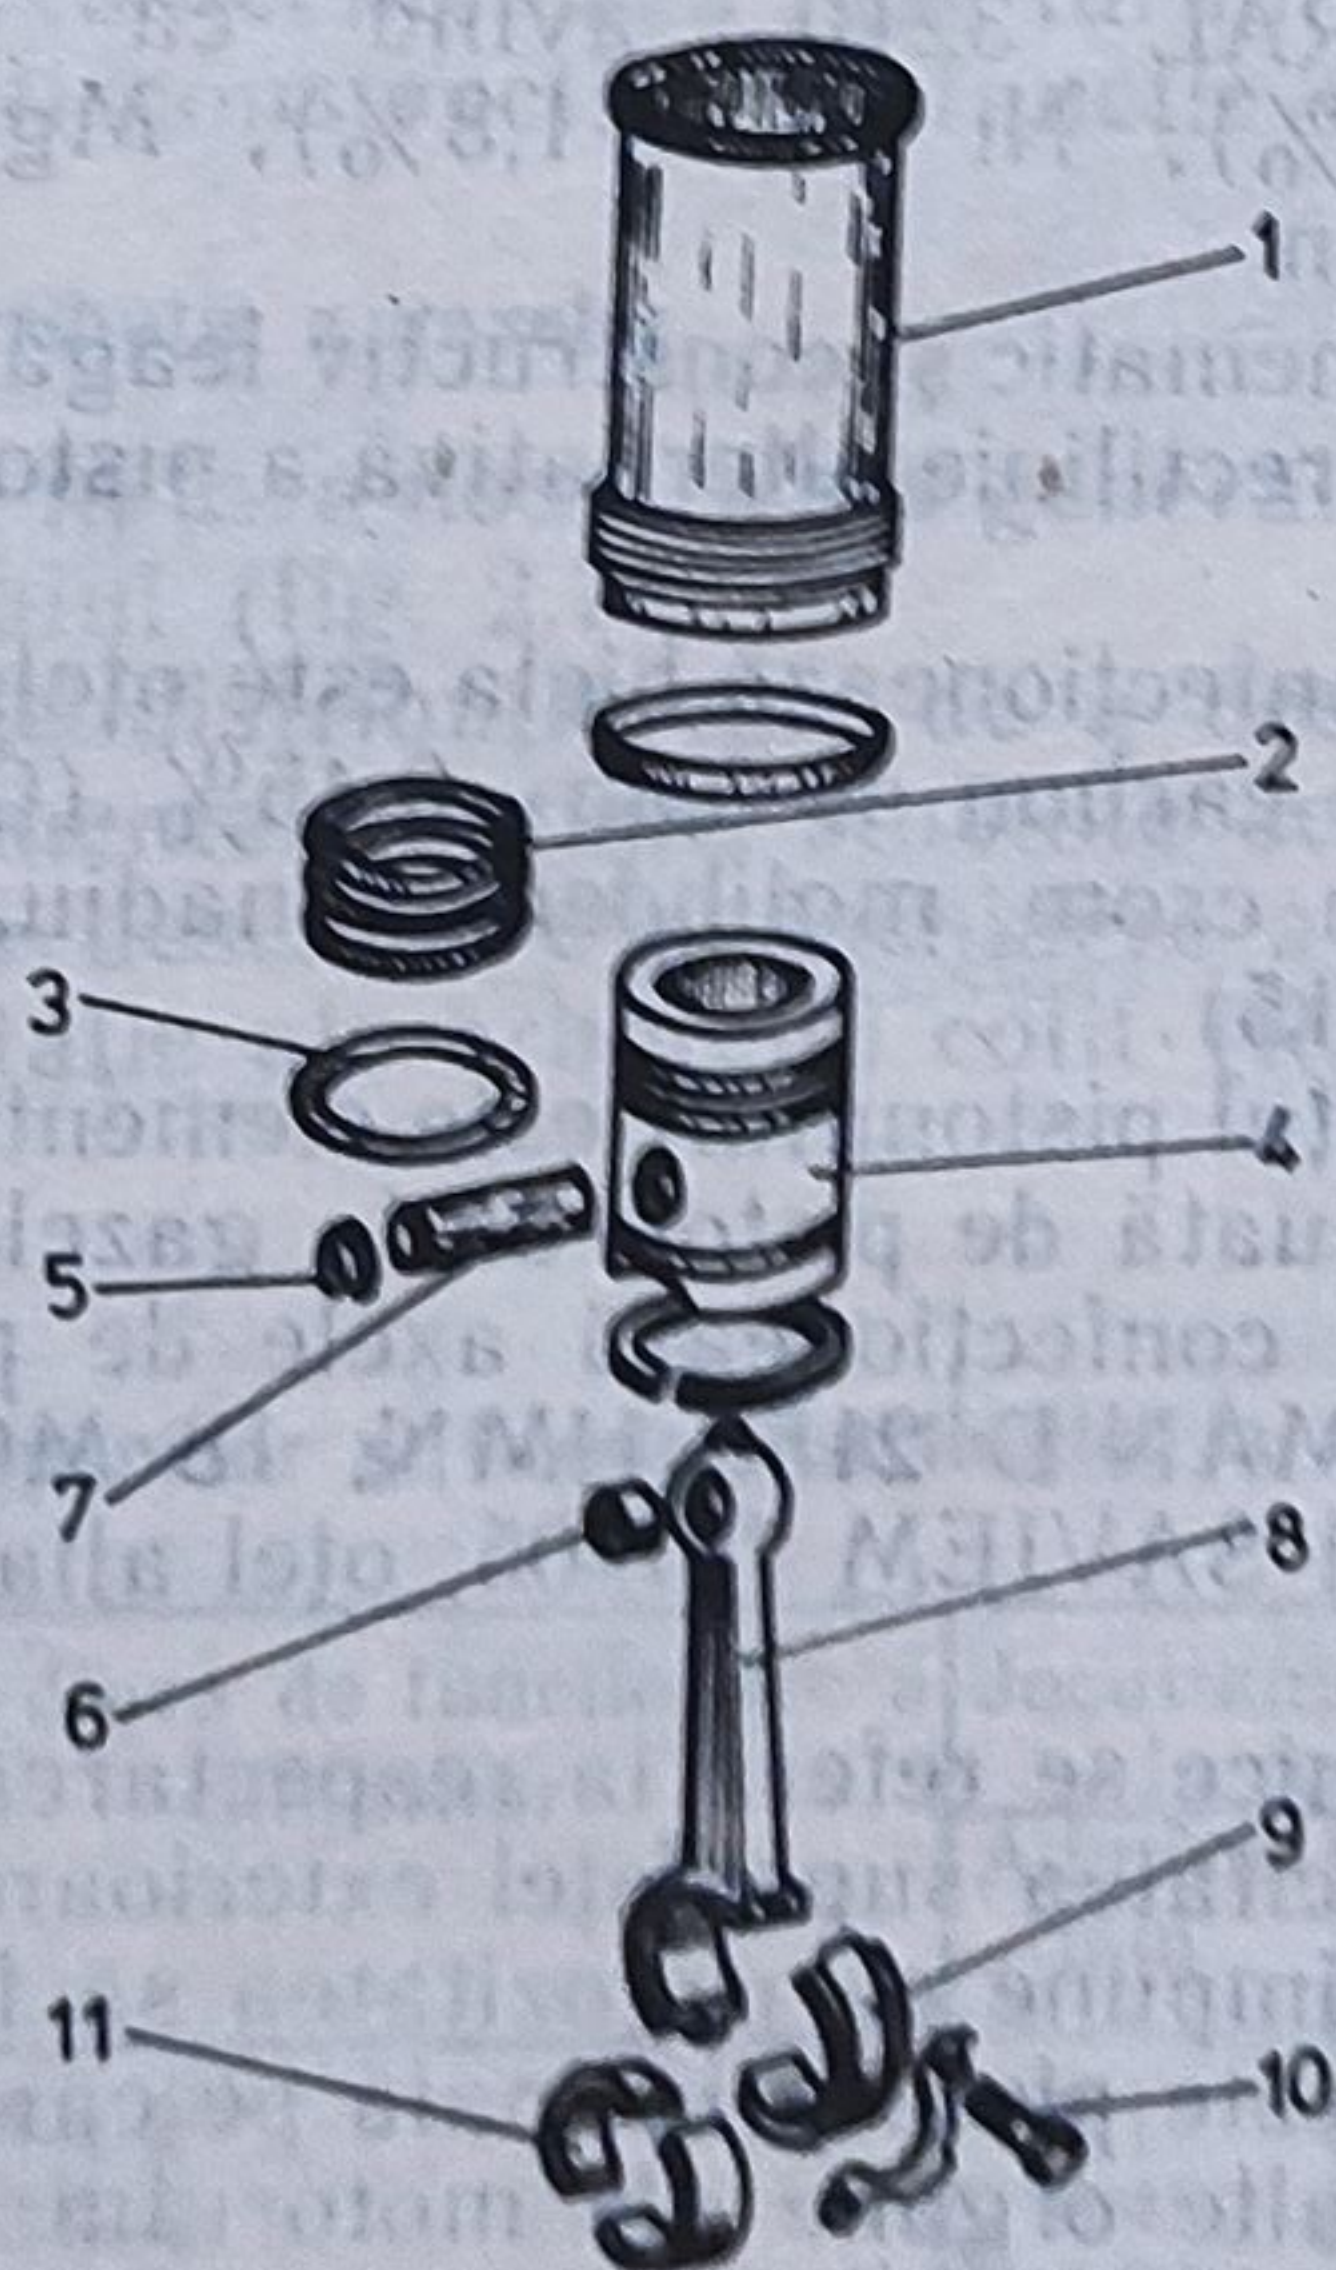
Grupul cilindru-piston-bielă: 1 — cămașa de cilindru; 2 — segmenti de compresie; 3 — segmenti de ungere; 4 — piston; 5 — inele pentru bolțul pistonului; 6 — bușă pentru bolțul de piston; 7 — ax de piston (bolț); 8 — bielă; 9 — capacul bielei; 10 — șuruburi pentru asamblarea capului bielei; 11 — semicuzineți.
